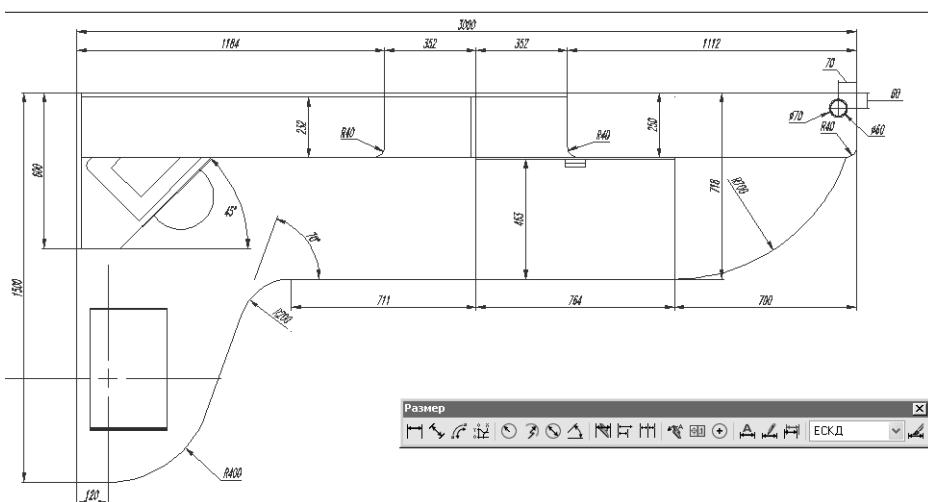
▼ Чертеж с нанесенными радиусами, диаметрами и угловыми размерами
